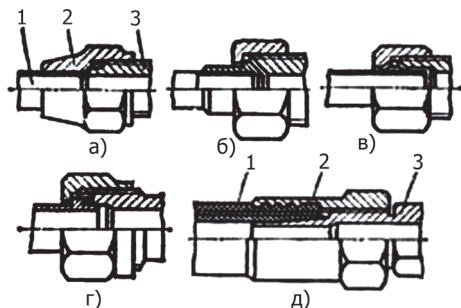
Схемы соединения трубопроводов и рукавов с помощью арматуры
